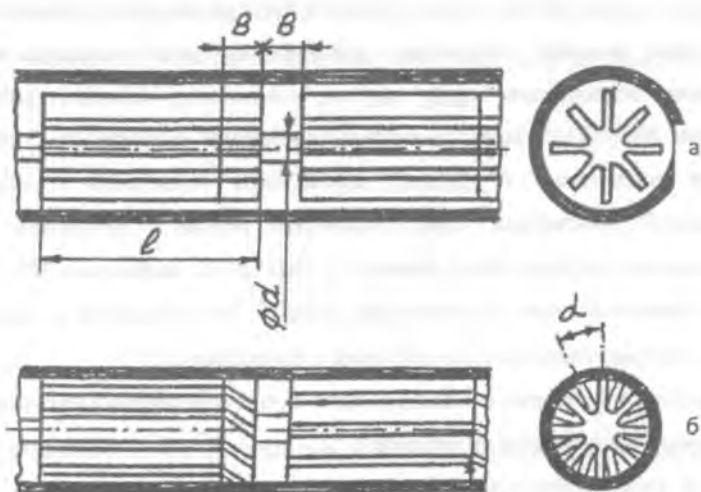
Конструкция заготовки (а) и готовой многоканальной трубы (б)
